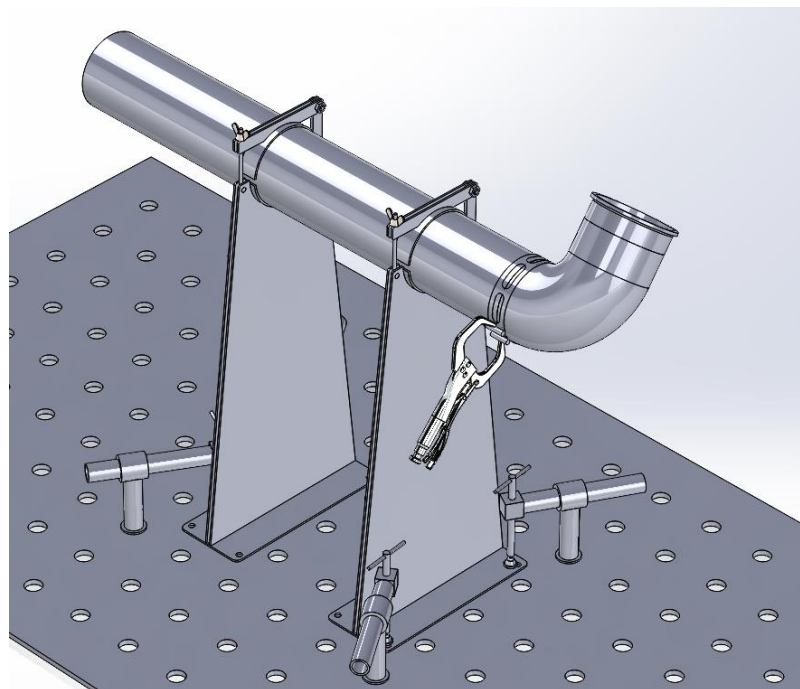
Розташування заготовок та притискачів в середині камери при зварюванні шва № 4
